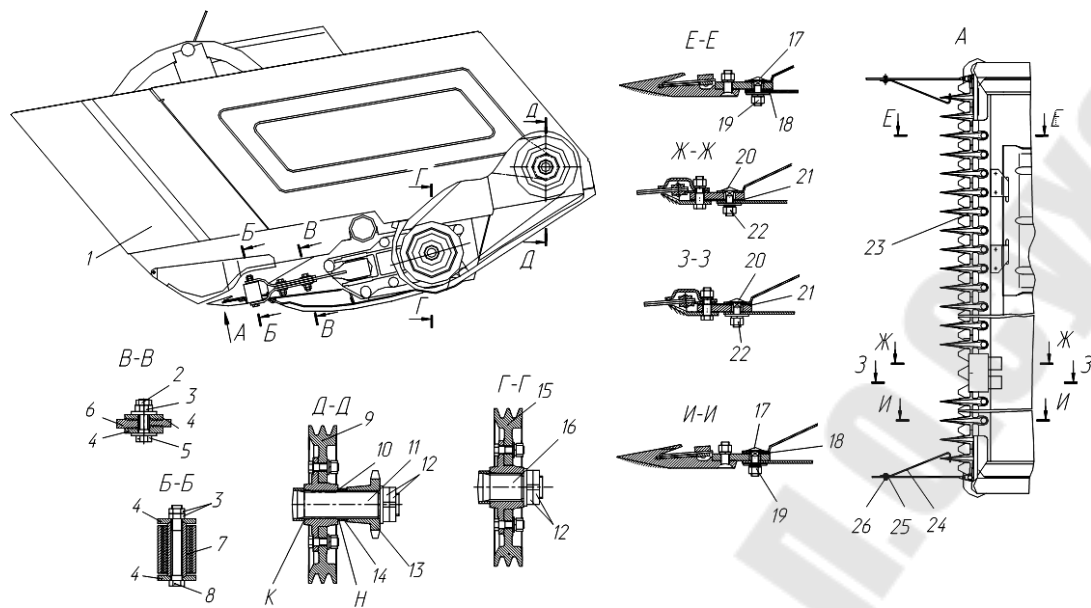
Схема сборки и регулировки пальцевого аппарата жатки для трав: 1 – жатка; 2, 3, 12, 19, 22, 26 – гайки; 4 – накладки; 5, 8, 17, 20, 25 – болты; 6 – рычаг; 7 – головка ножа; 9, 15 – шкивы; 10 – прокладка регулировочная; 11 – контрпривод; 13 – звездочка; 14 – втулка; 16 – привод режущего аппарата; 18, 21 – прокладки; 23 – аппарат пальцевый режущий; 24 – стеблеотвод
